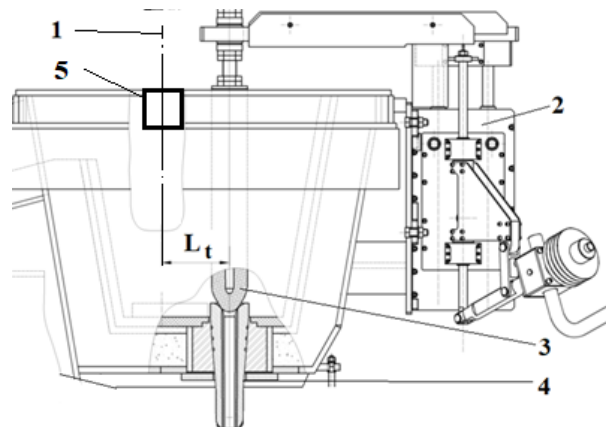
Общий вид системы сталеразливочный ковш – промежуточный ковш перед началом разлива:
